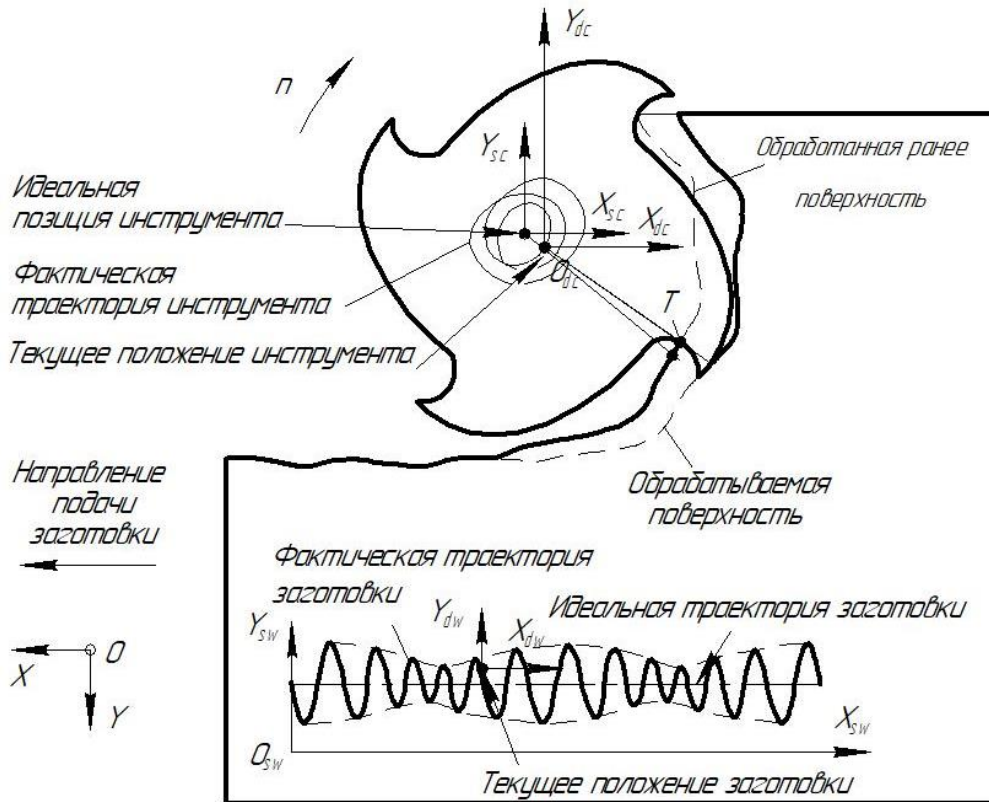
Внедрение фрезы в заготовку с учетом колебаний оси инструмента и заготовки
